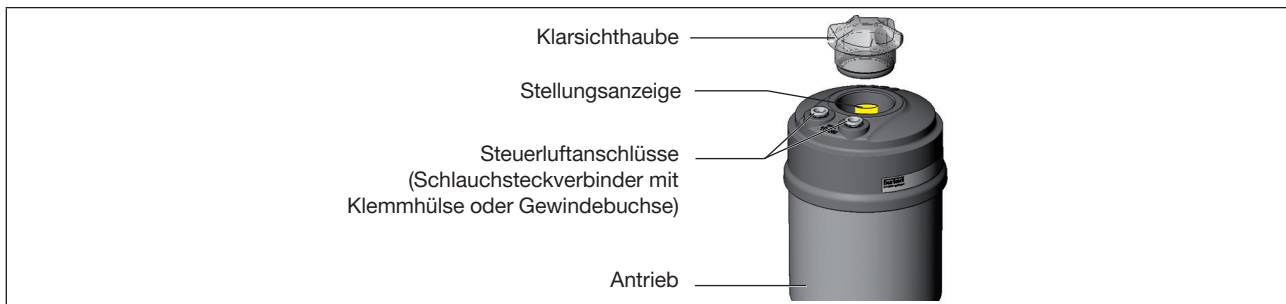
Schaltspindel montieren (1), integrierte Steuerluftführung
